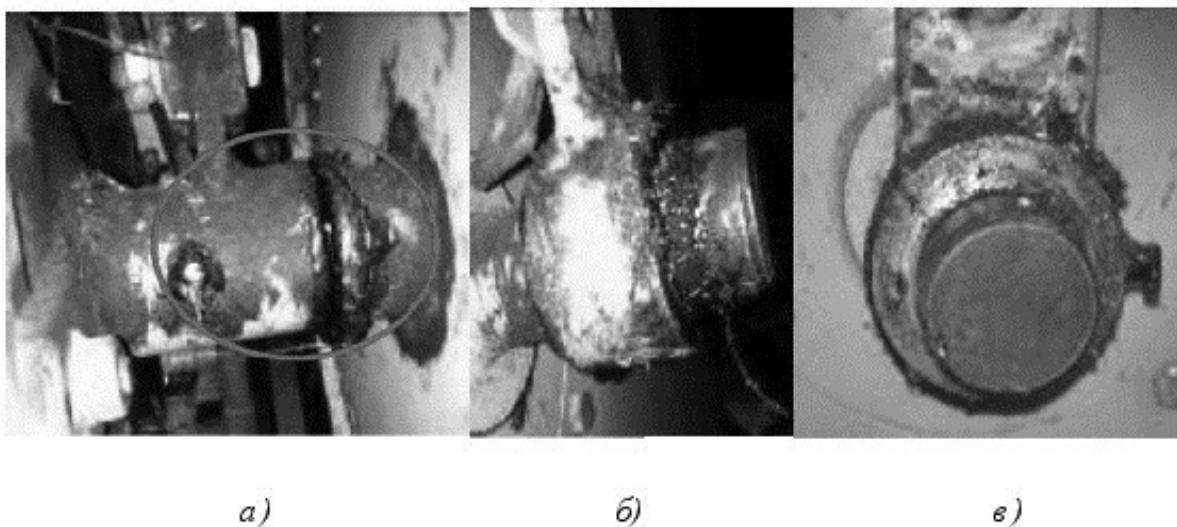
Подшипниковый узел трения скольжения:
